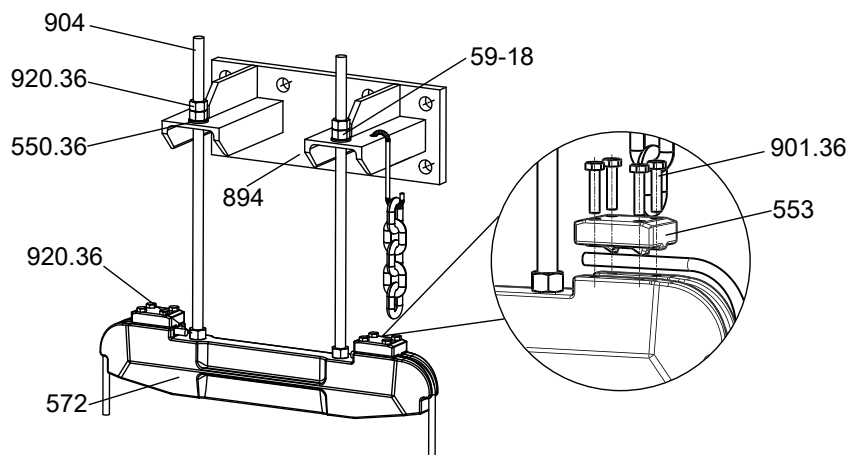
Konsolenvariante für Baugrößen mit Druckstutzen-Nenndurchmesser DN 350, DN 400, DN 500, DN 600 und DN 700
